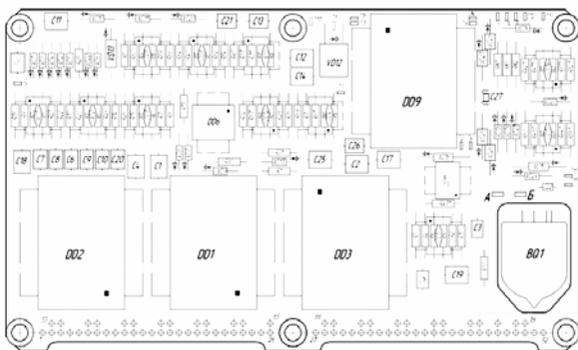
Фрагмент сборочного чертежа электронного блока 2
